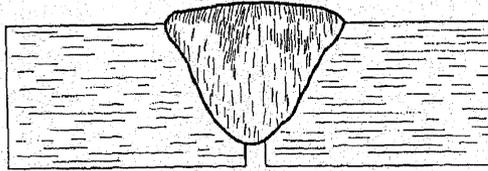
Sección transversal de la soldadura en la que se muestra una inadecuada penetración en la unión
